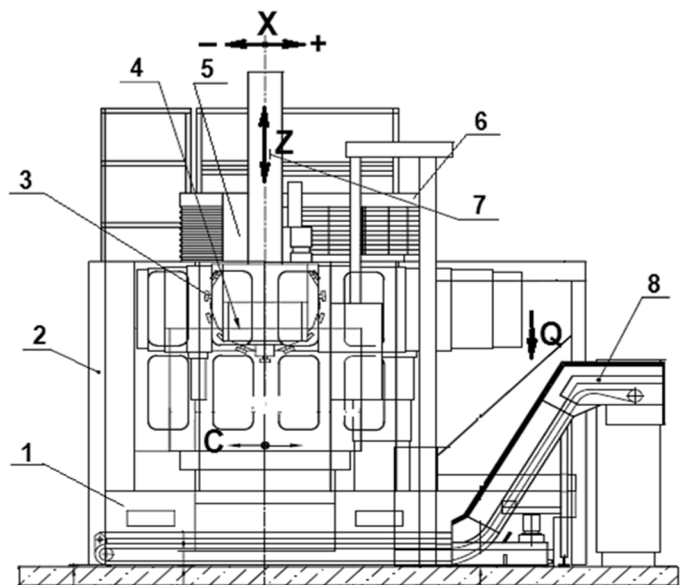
Вертикальний токарний верстат SKIQ
